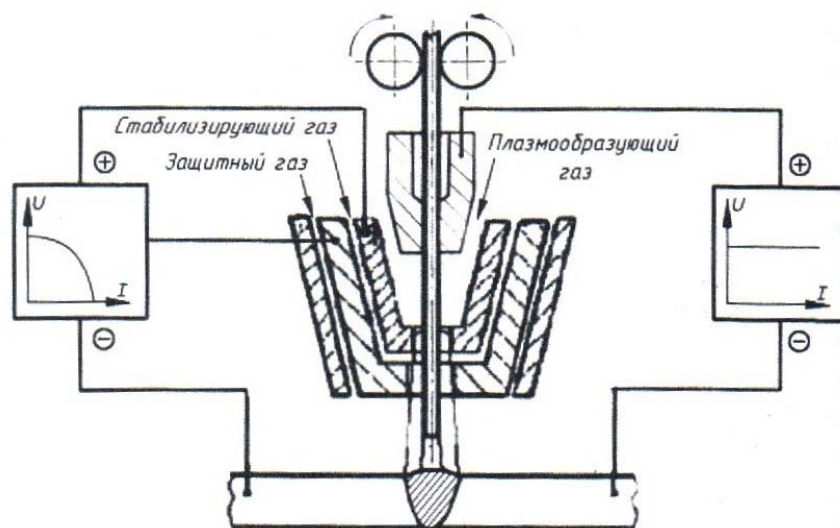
Схема процесса плазменной сварки плавящимся электродом
